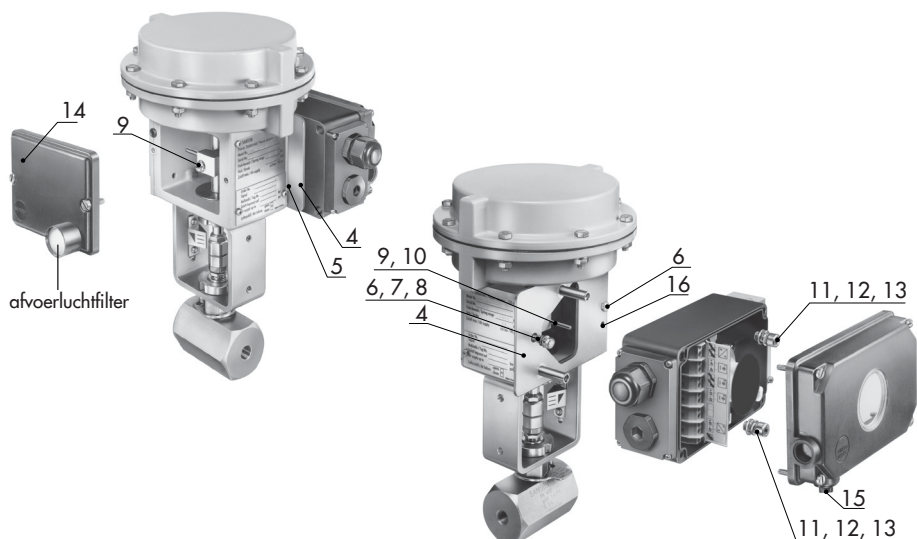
Montage aan SAMSON-slaandrijving type 3277-5 · interne instrumentenluchttoevoer
